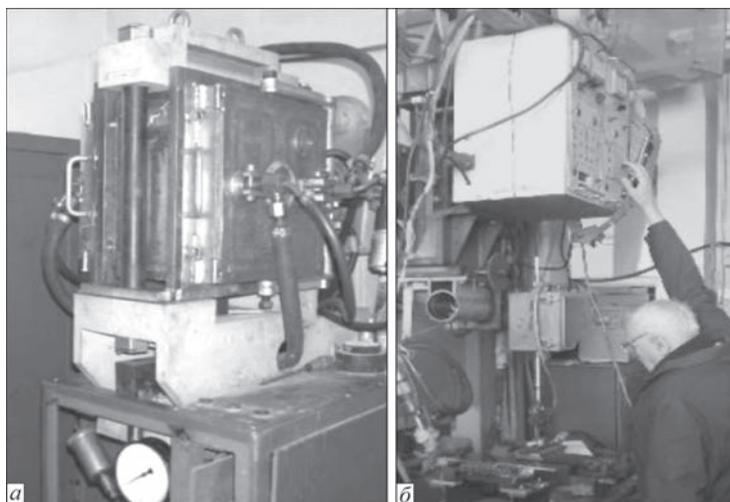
Оборудование для сварки с различными скоростями нагрева: а — установка П-115; б — лабораторная установка
